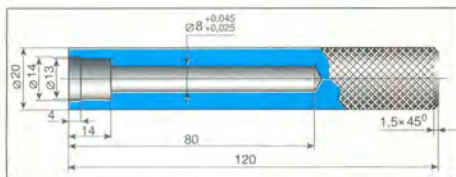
Оправка для напрессовки колпачка на направляющую втулку клапана.
